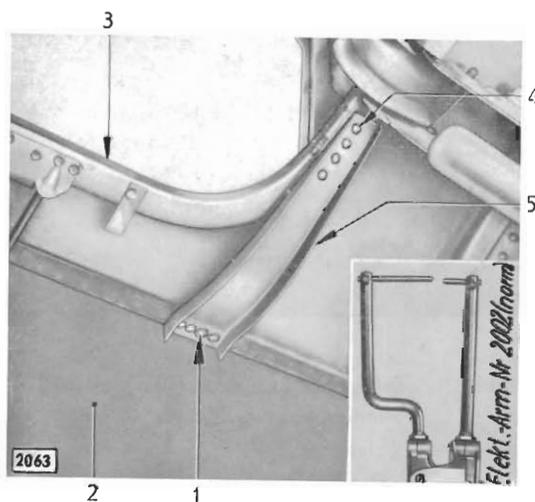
Stütze für Karosserierückwand an Seitenwand und U-Sicke der Karosserierückwand zangenpunktgeschweißt
